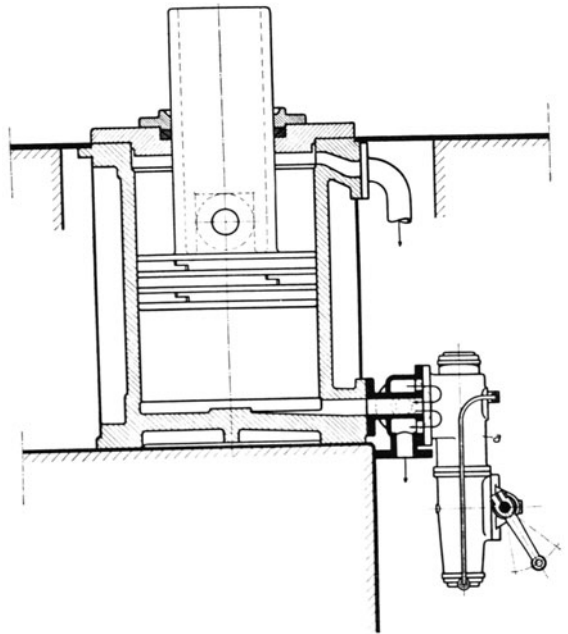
Einlaßbremse mit Bremsdruckregler.
